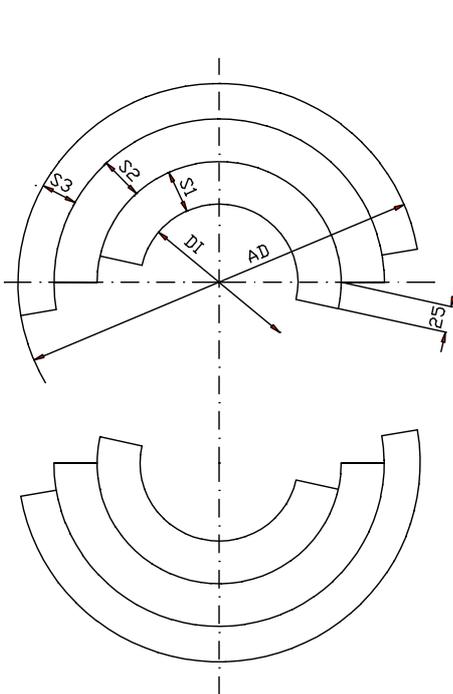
Aufbau einer dreilagigen Isolierschale
